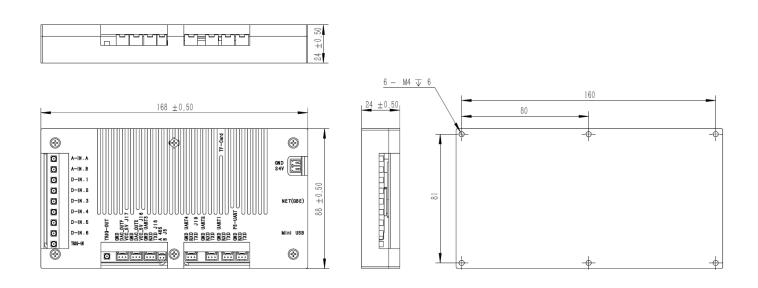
SPCB-NET-B 外部尺寸图 (单位: mm)
